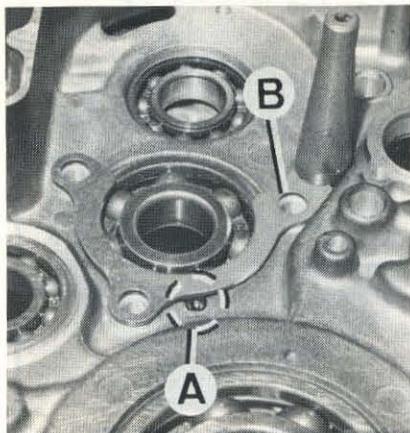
A. Ergot du roulement droit d'arbre primaire - B. Plaquette de calage latéral (Photo RMT)
